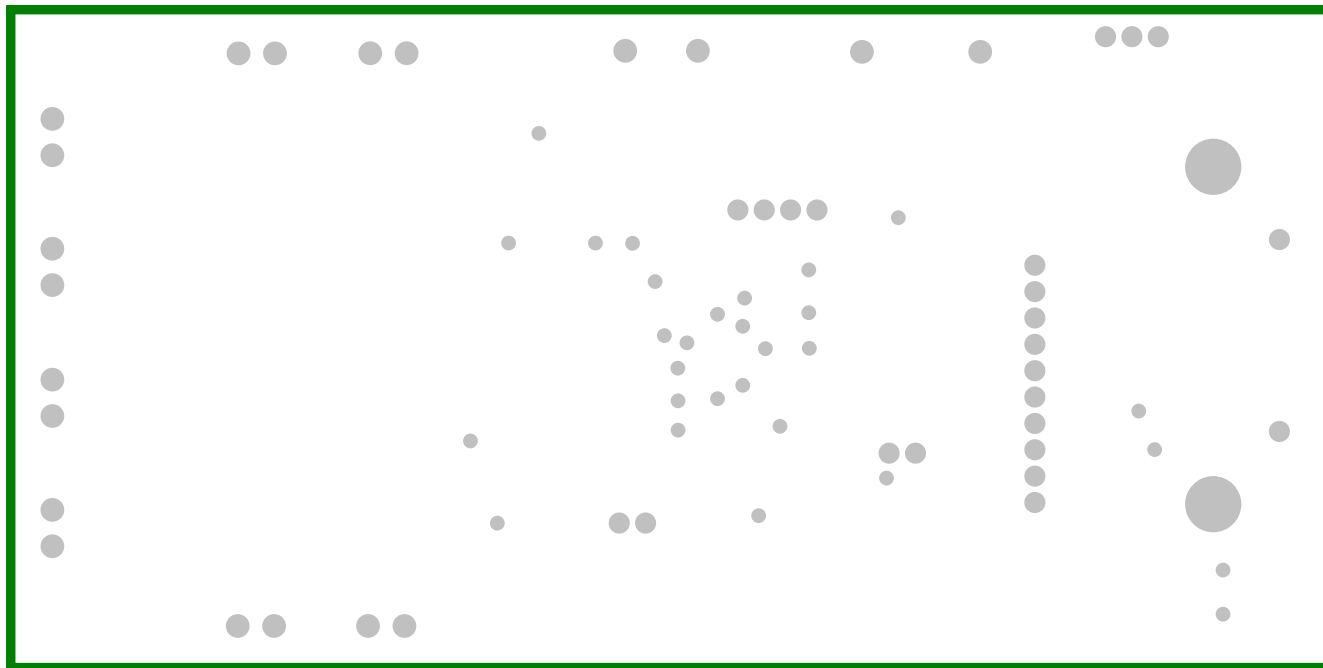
ADS131E08EVM 的 PCB 布局 (内部 AVSS/GND 平面 1)
